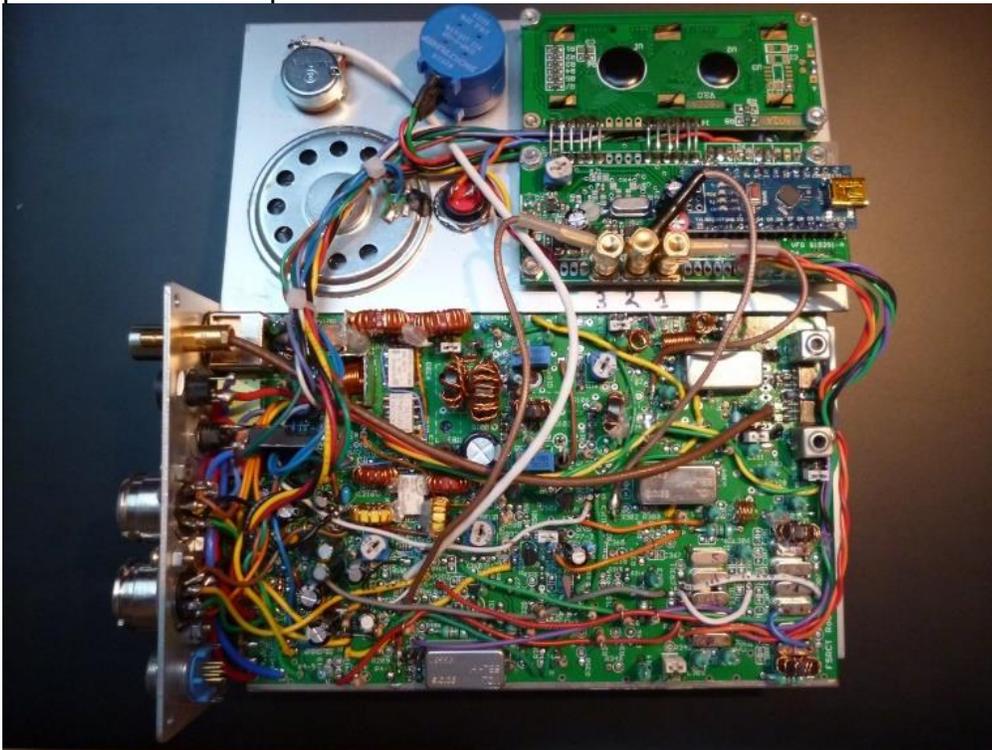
Vue d'ensemble interne du Rocket dans sa première version A.
